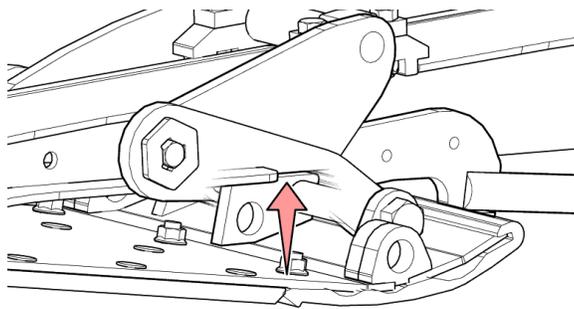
Точка контакта копирующего башмака тянущего типа
